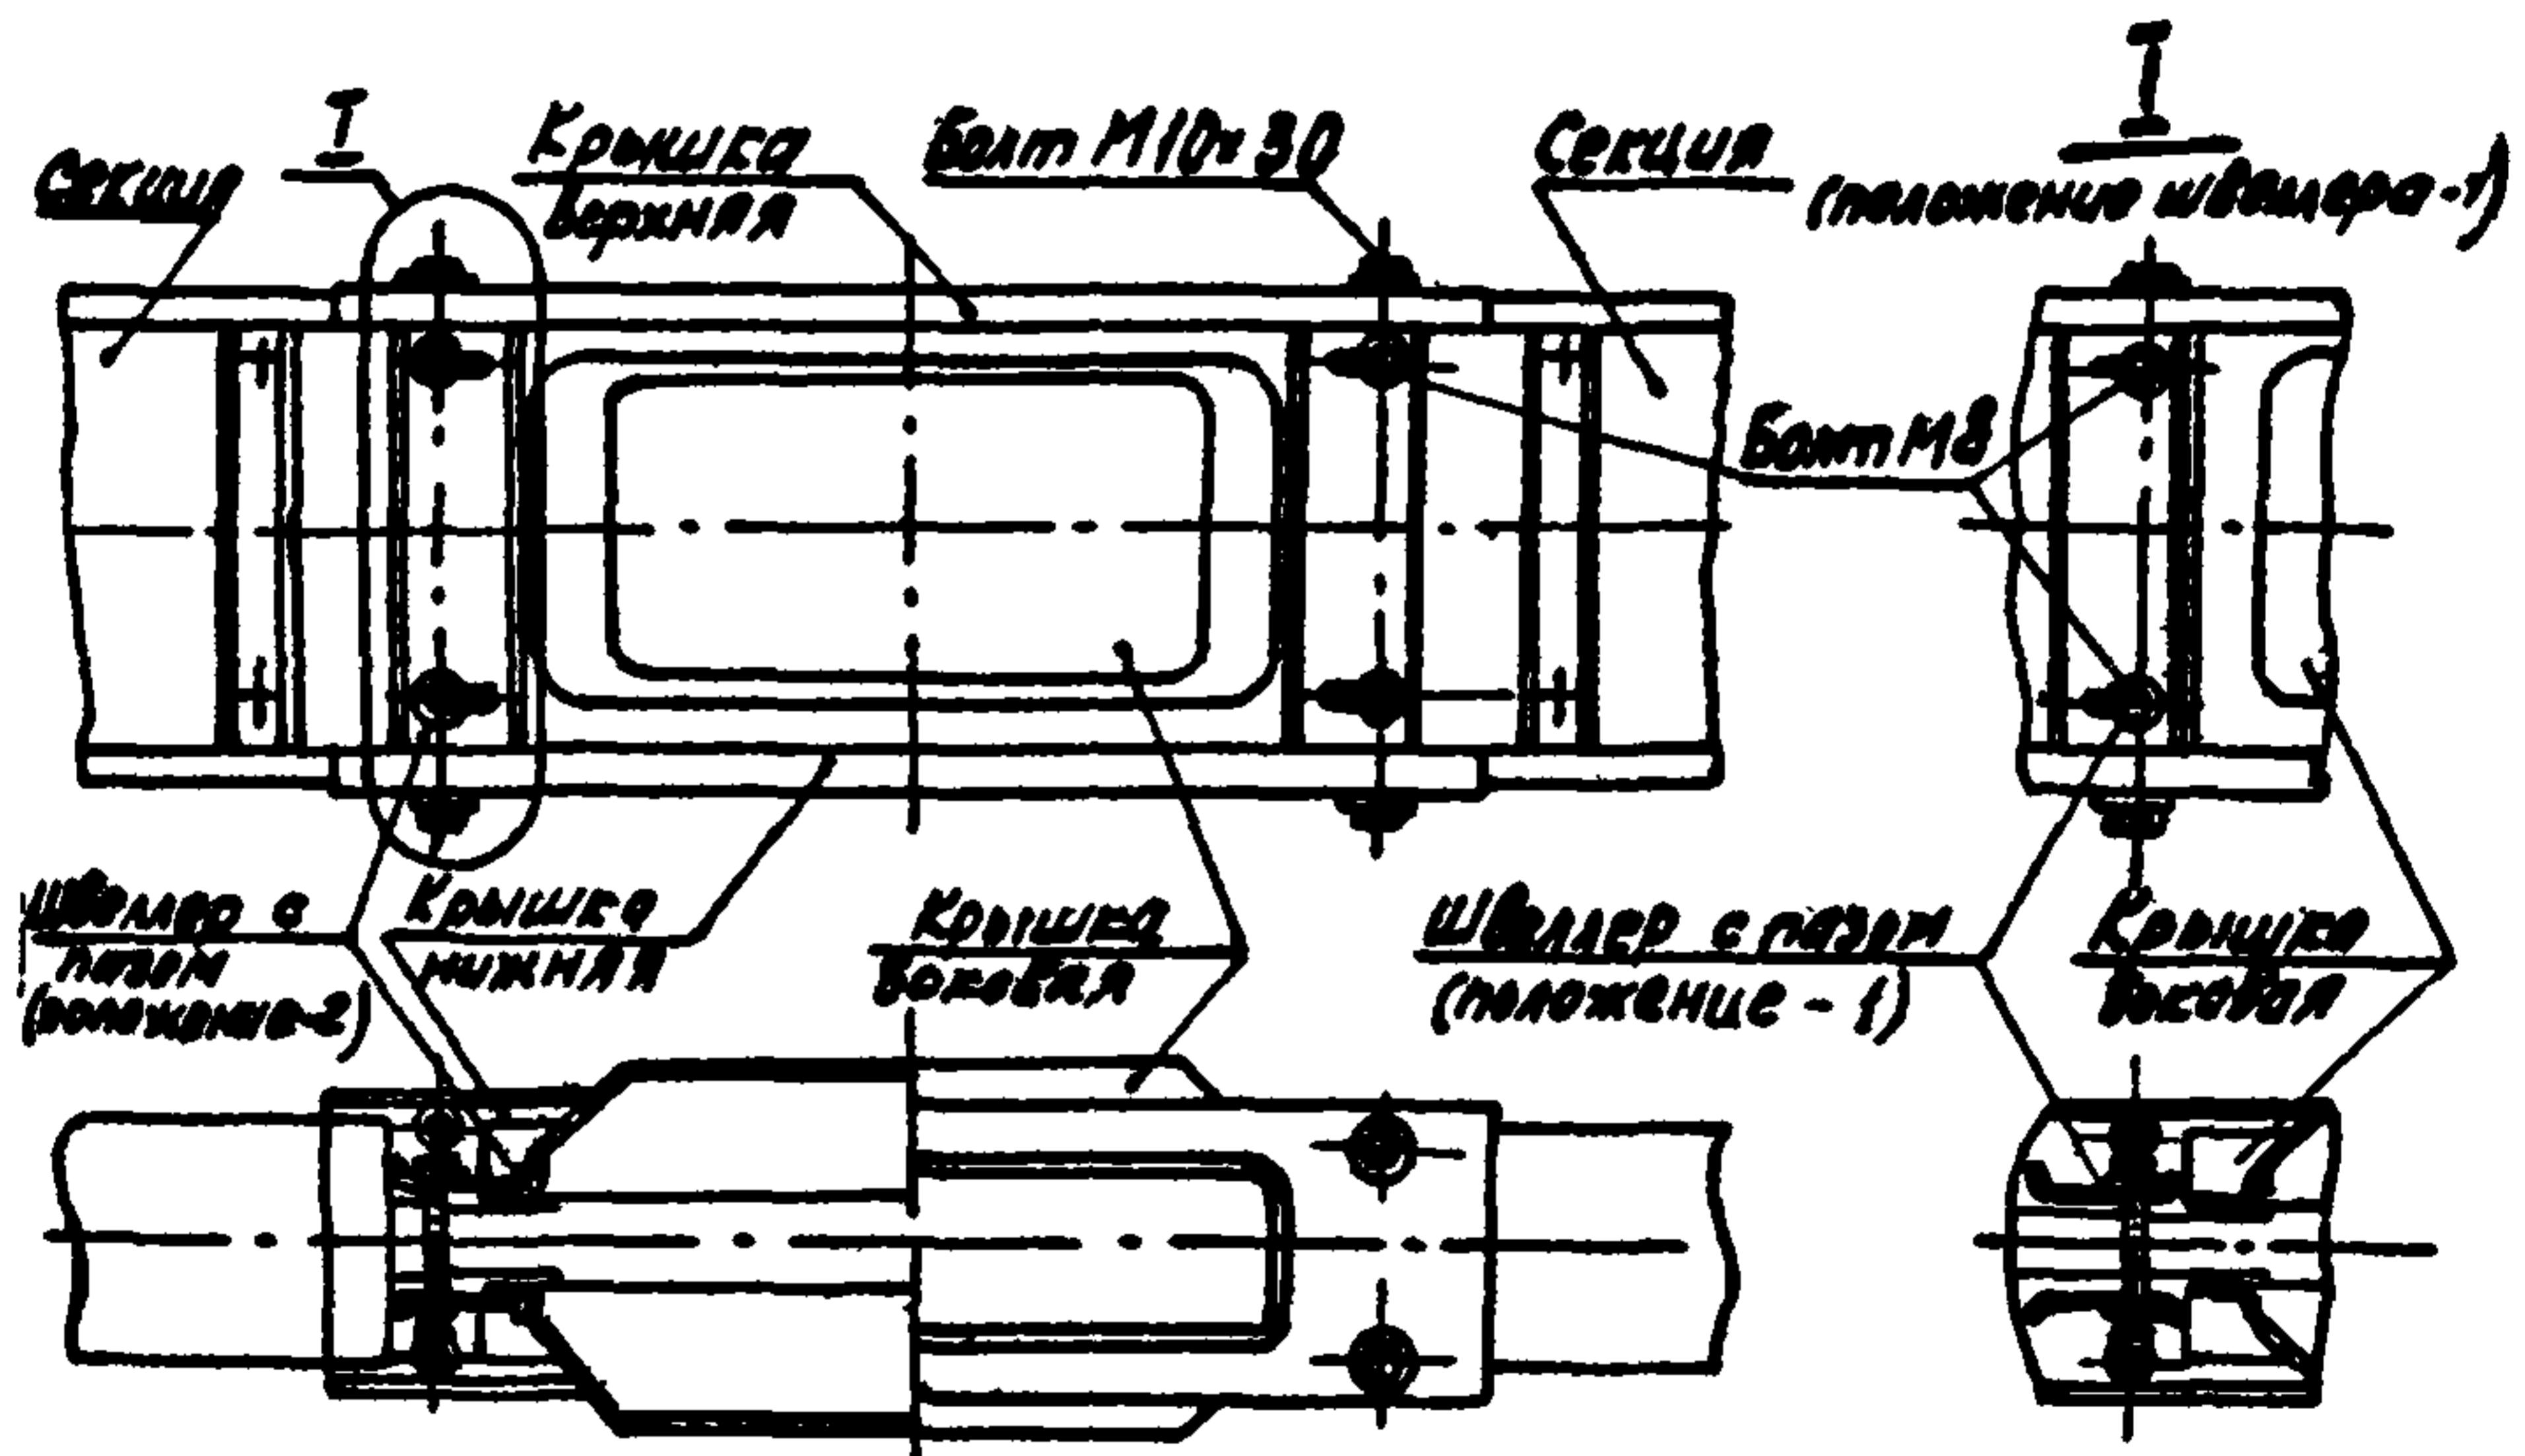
Сборка стыковочного комплекта при сварном соединении шин
